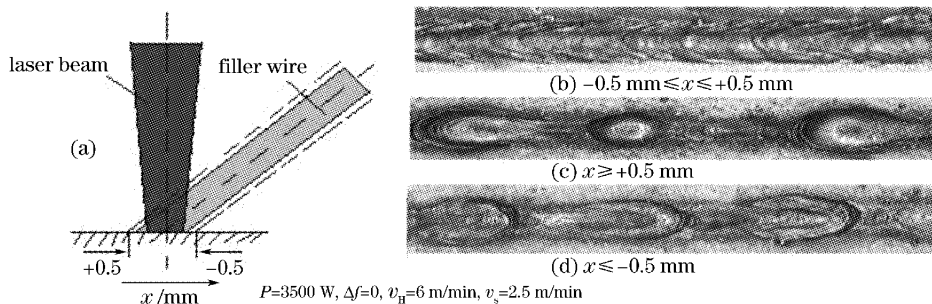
焊丝相对于激光束的位置对焊缝成形的影响
